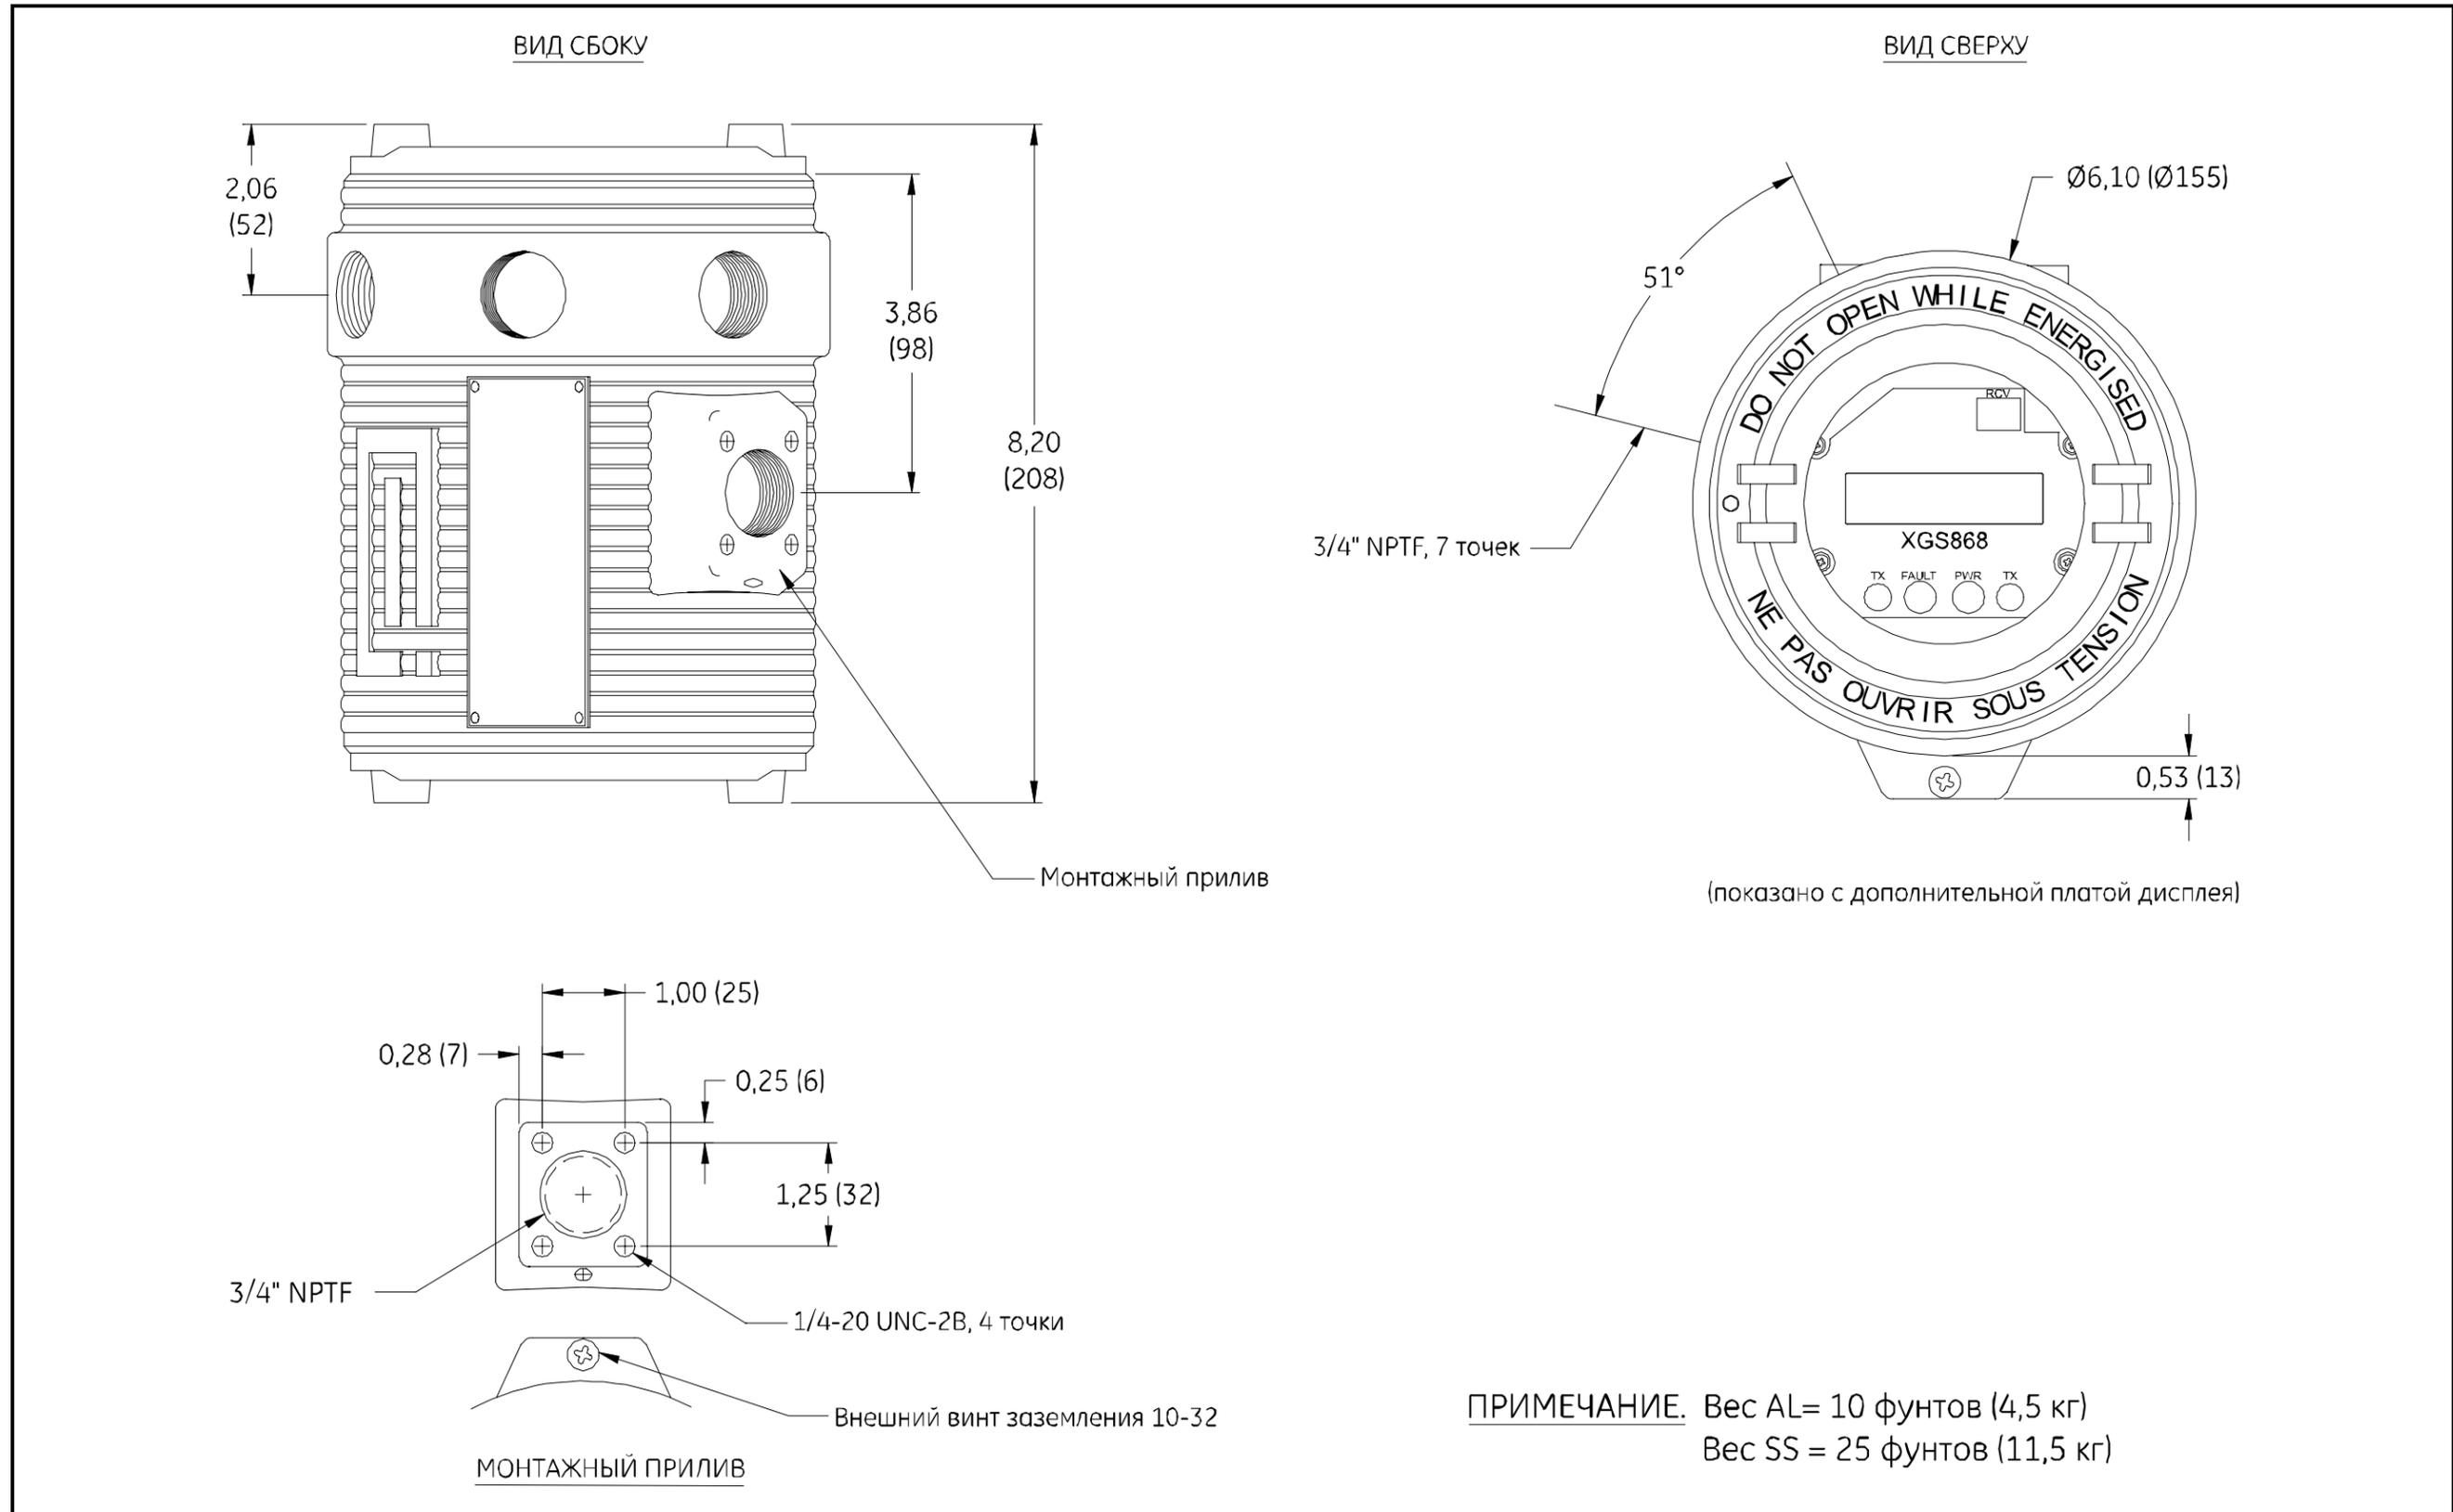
Габаритный чертеж (№ 712-1002)
